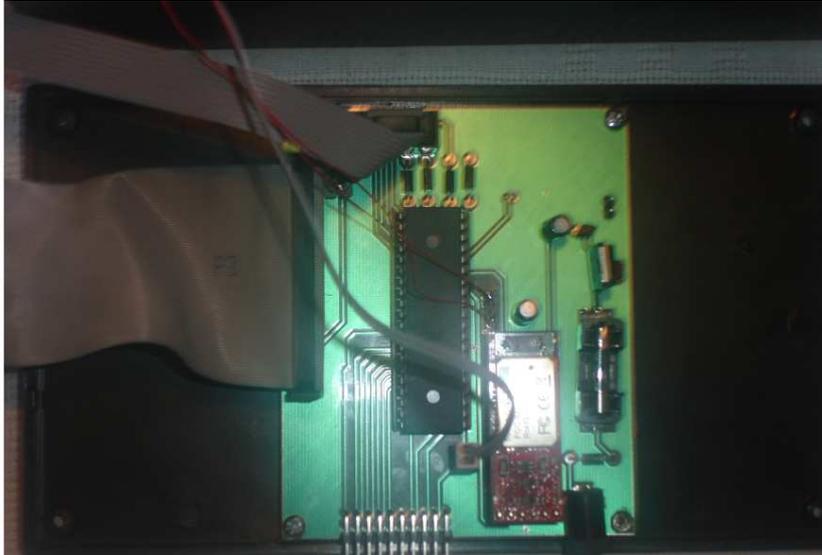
Montaje del PCB del PDAT164P en la caja
